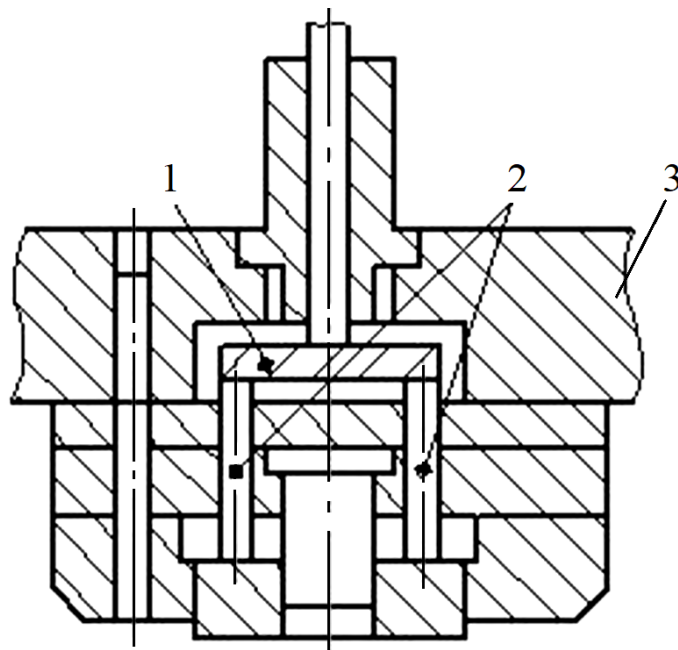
Загальний вигляд вузла виштовхування штампа:
